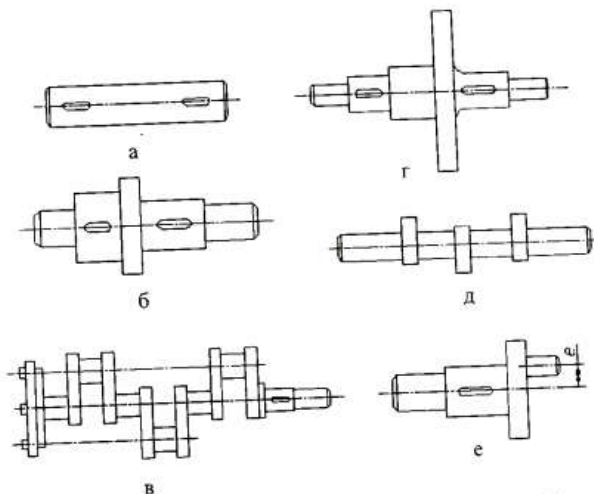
Конструктивні види валів: а – гладкий вал; б – ступінчастий вал; в – колінчастий вал; г – дисковий вал; д – кулачковий вал; е – кривошипний вал
